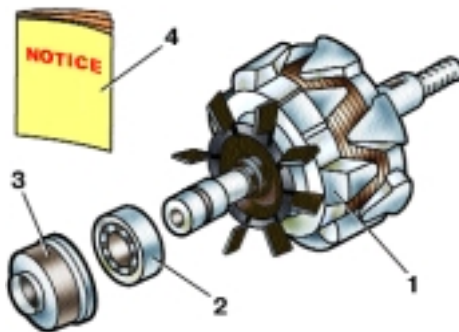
Комплект ротора (77 01 204 725): 1 – ротор; 2 – подшипник генератора; 3 – пылезащитный чехол подшипника; 4 – инструкция
